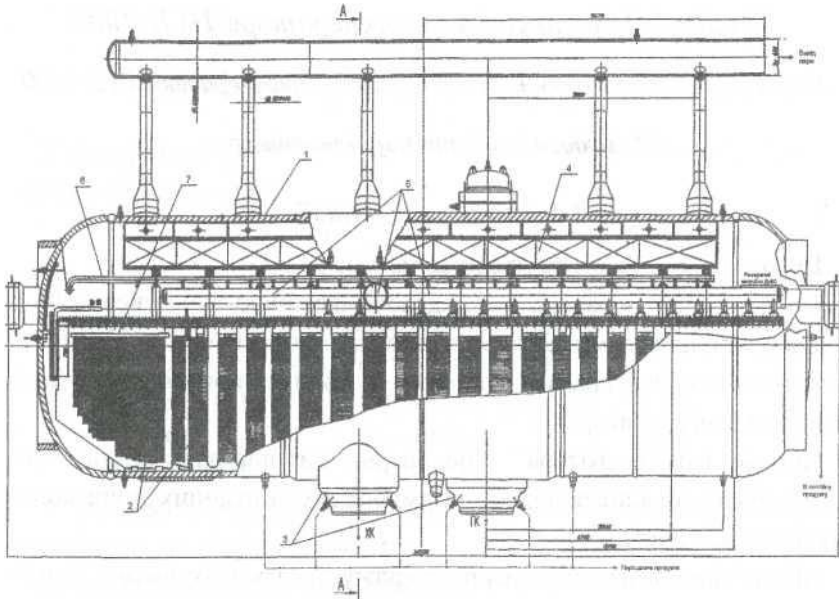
Розріз корпусу парогенератора ПГВ-1000:
